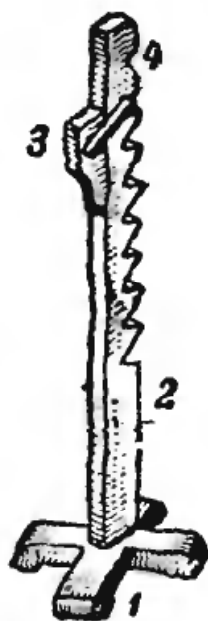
Подставка (козелки) для поддержки заднего конца длинных деталей, зажатых в передние тиски верстака: 1 — крестовина; 2 — стойка с зубцами; 3 — опорная колодка; 4 — хомут для постановки опорной колодки.
